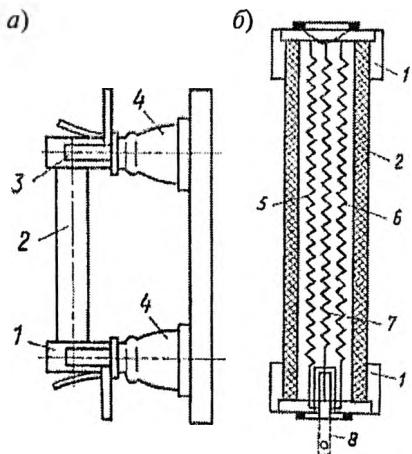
Кварцевый предохранитель ПК на 10 кВ: а – внешний вид установки; б – разрез
